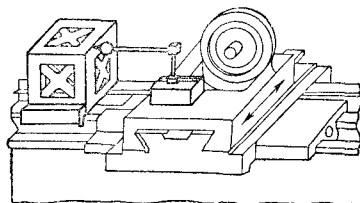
Проверка перпендикулярности направляющих колонны к столу у зубофрезерного станка.
